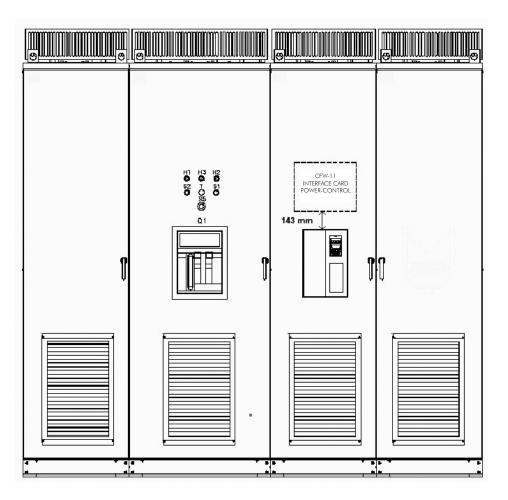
Ejemplo de montaje del rack de control y su base
